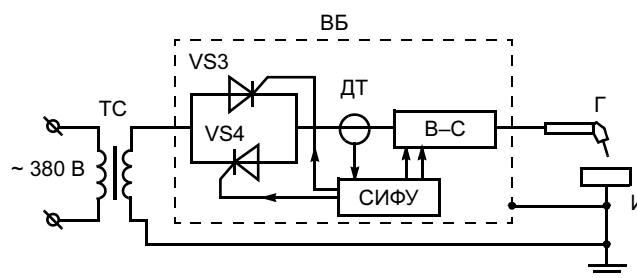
Схема установки для аргонодуговой сварки металлов переменным током с тиристорным регулятором тока сварки (*ТС* — силовой трансформатор; *ВБ* — выносной блок; *В-С* — возбуждительно-стабилизатор сварочной дуги; *ДТ* — датчик тока; *VS3, VS4* — тиристоры; *Г* — горелка; *И* — изделие)
